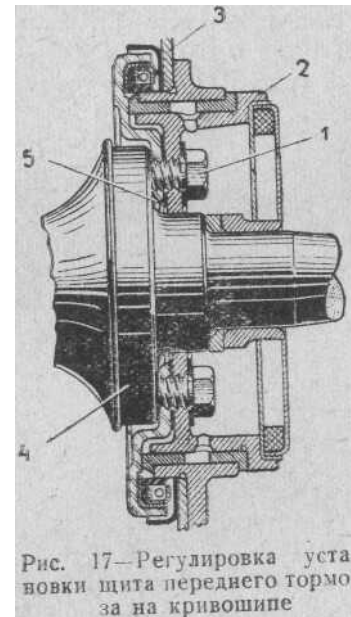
Регулировка установки шита переднего тормоза на кривошипе
